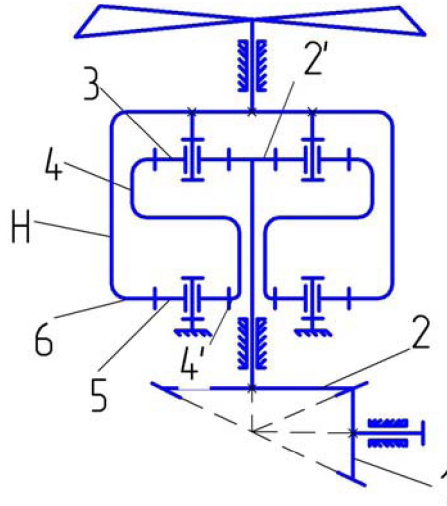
Схема редуктора двигателя вертолёта МИ – 6
